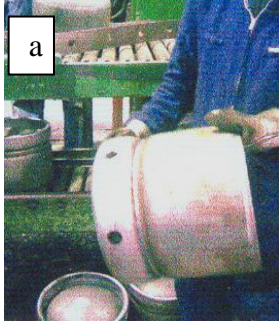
Dressage et soudage des deux embouts et de la collerette.
